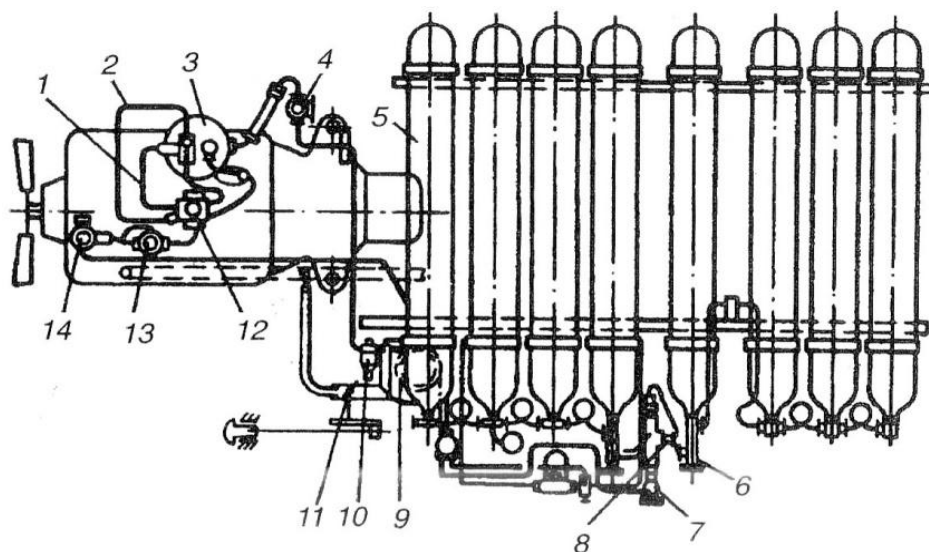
Схема системы питания сжатым газом: 1 – трубка холостого хода; 2 – трубка для основной подачи газа; 3 – редуктор низкого давления; 4 – электромагнитный клапан; 5 – баллон; 6 – расходный вентиль; 7 – вентиль заправочный; 8 – предохранительный клапан; 9 – подогреватель; 10 – редуктор высокого давления; 11 – заслонка подогревателя; 12 – карбюратор-смеситель; 13 – бензиновый клапан-фильтр; 14 – бензонасос
